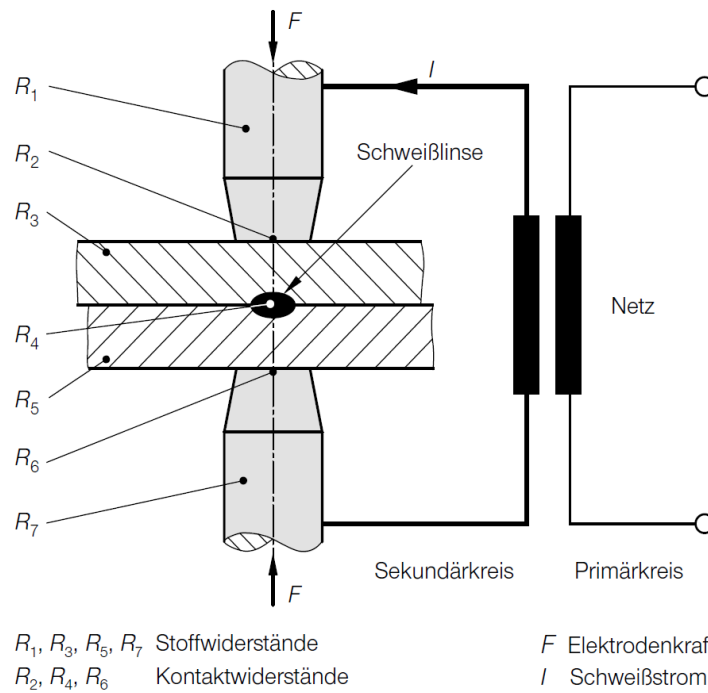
Verfahrensprinzip Widerstandspunktschweißen [5]
